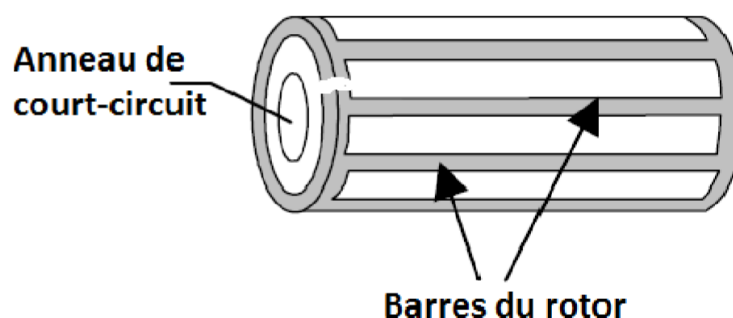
Défaut d'un rotor à cage d'écureuil; rupture d'anneau de court-circuit.
